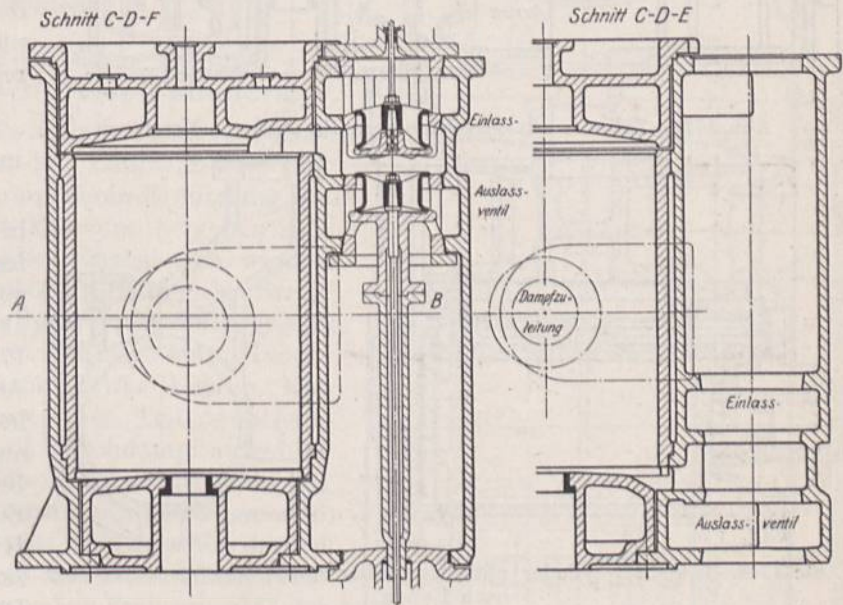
Zylinder mit Ventilsteuerung für stehende Maschinen.
